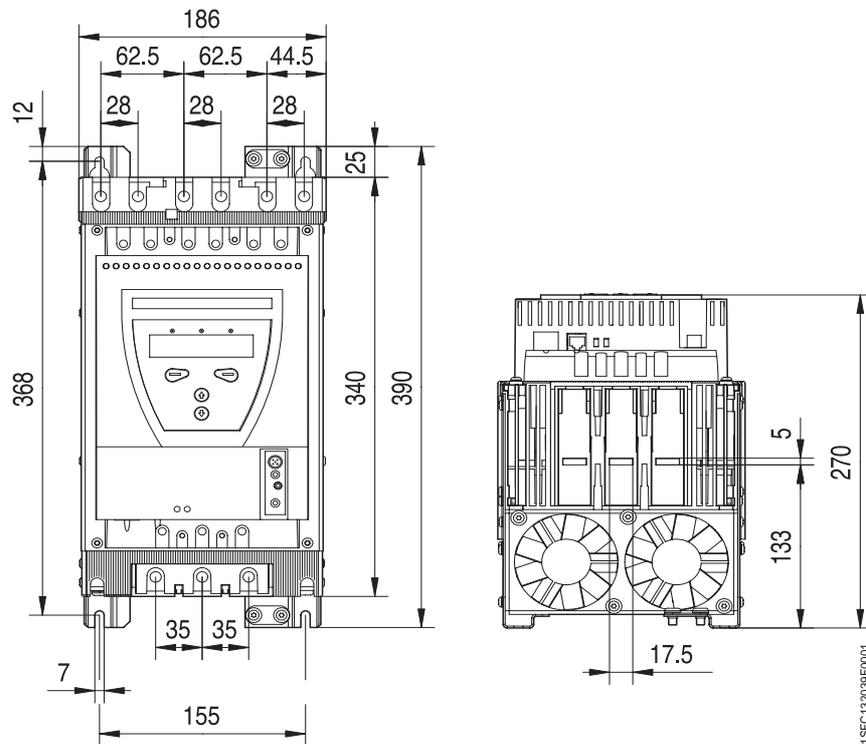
Dimensions PST85...142 (mm) (1 mm = 0,0394 pouce)
